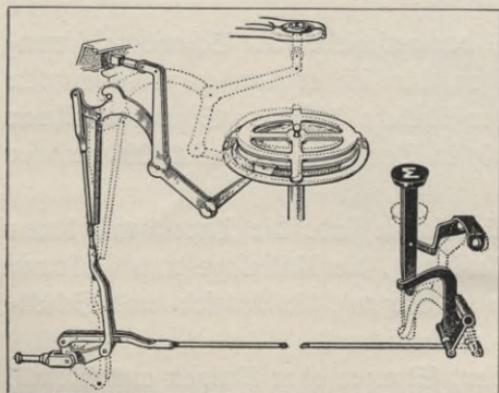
Hebelmechanismus zur Yost-Maschine.
